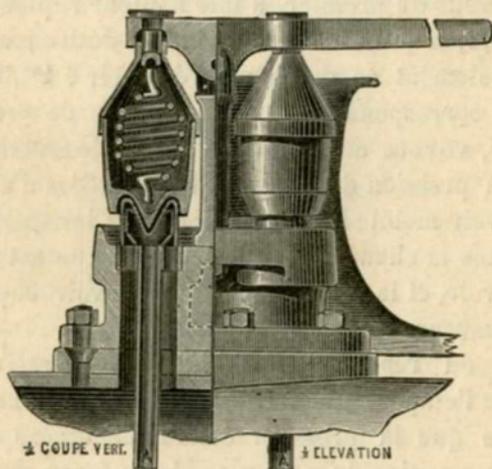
Soupape de sûreté (coupe verticale et élévation).
